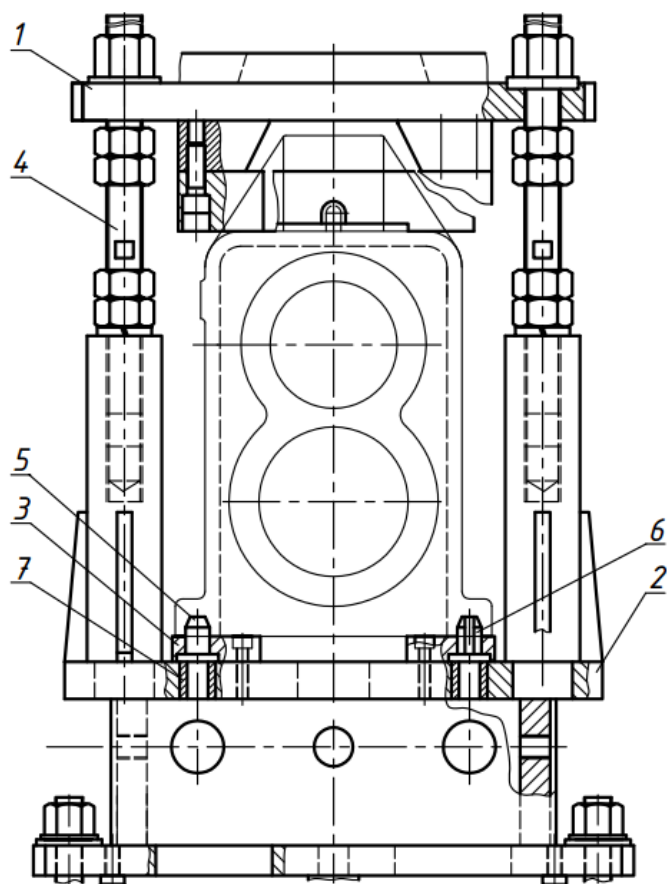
Конструкція пристрою для комплексної обробки деталі
